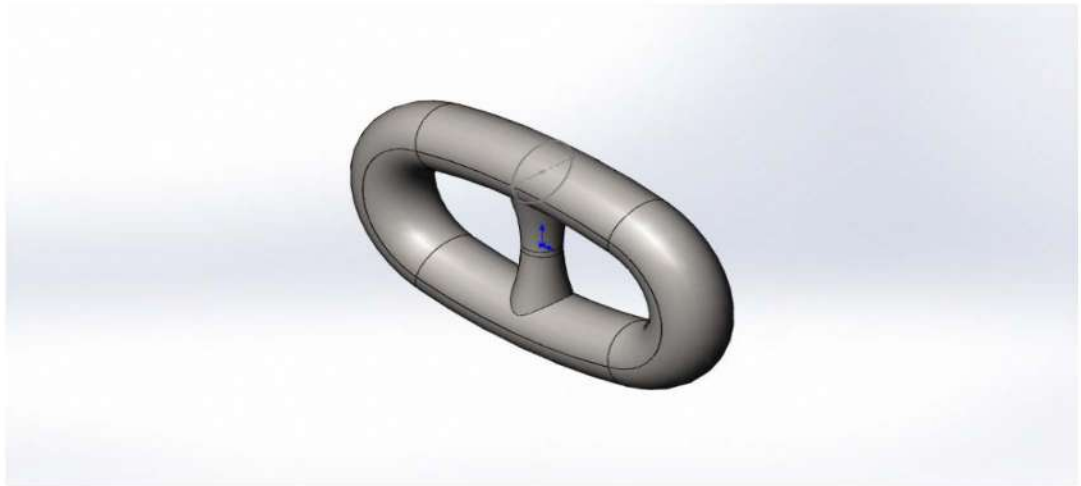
Загальний вигляд якірного звена с контрфорсом
